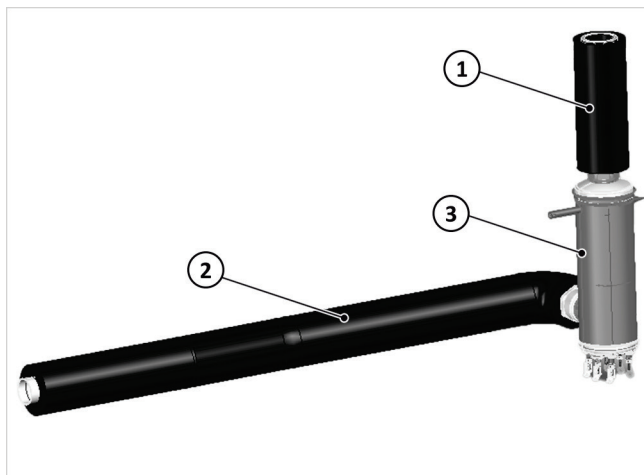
kit de conversion Max SL-7 (hydraulique)
